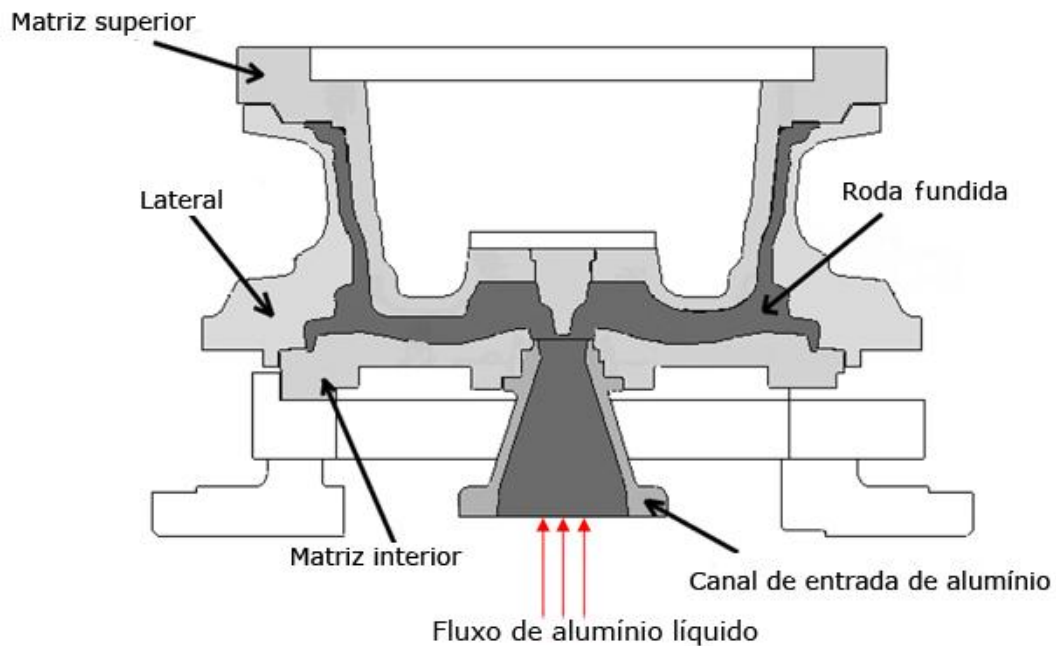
Desenho esquemático do conjunto de moldes e roda injetada mostrando a região de injeção.
